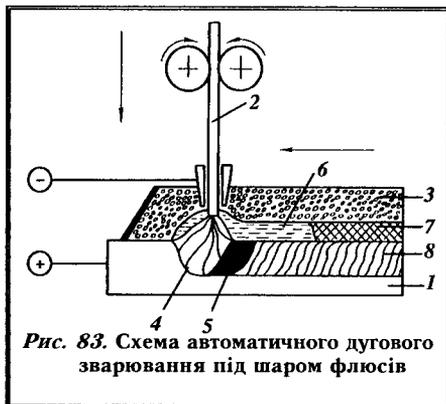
Схема автоматичного дугового зварювання під шаром флюсів
